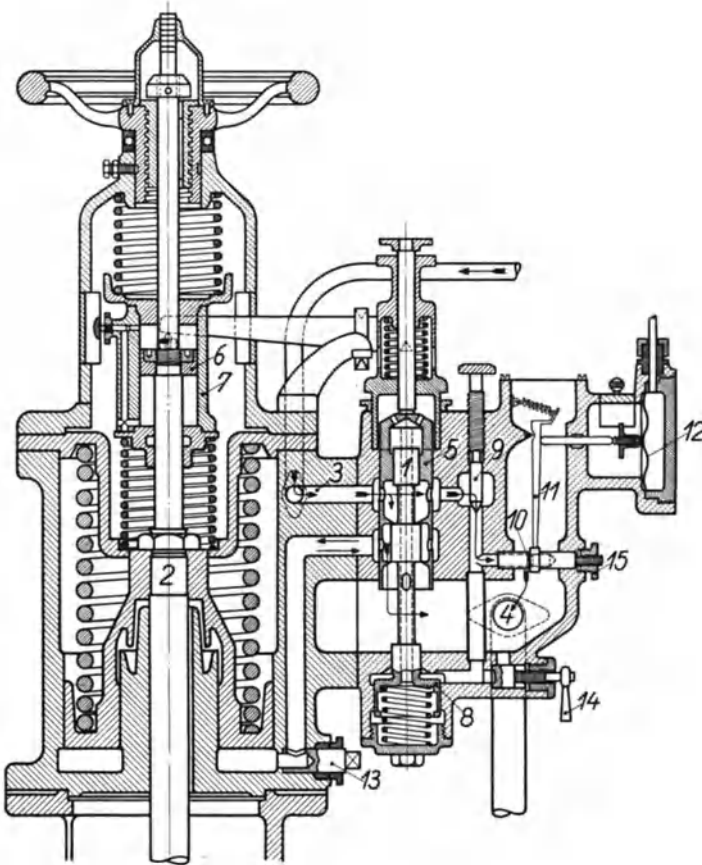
Steuerung des Avareglers mit Gleichdruckrückführung.
